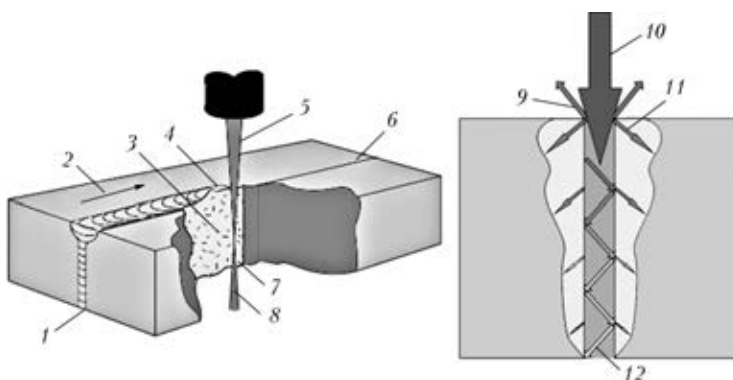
Схема процесса лазерной сварки с парогазовым каналом [4]: 1 — валик шва; 2 — направление сварки; 3 — ЗТВ; 4 — парогазовый канал; 5 — лазерный пучок; 6 — кромка шва; 7 — жидкий металл; 8 — лазерный пучок, выходящий из обрабатываемого изделия; 9 — отраженное излучение; 10 — лазерный пучок; 11 — поглощенное излучение; 12 — переотражения от стенок парогазового канала
